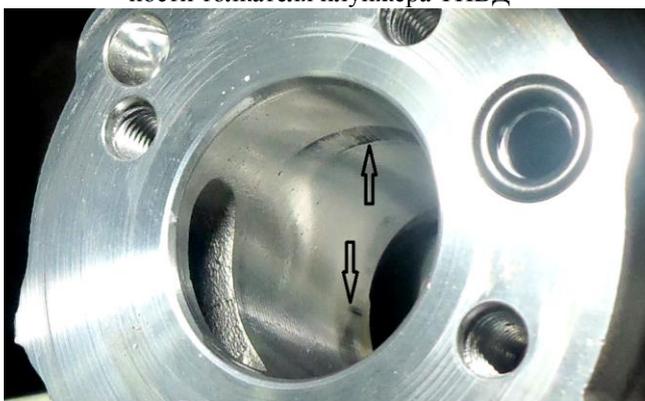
Натирь в отверстии под толкатель плунжера корпуса ТНВД
